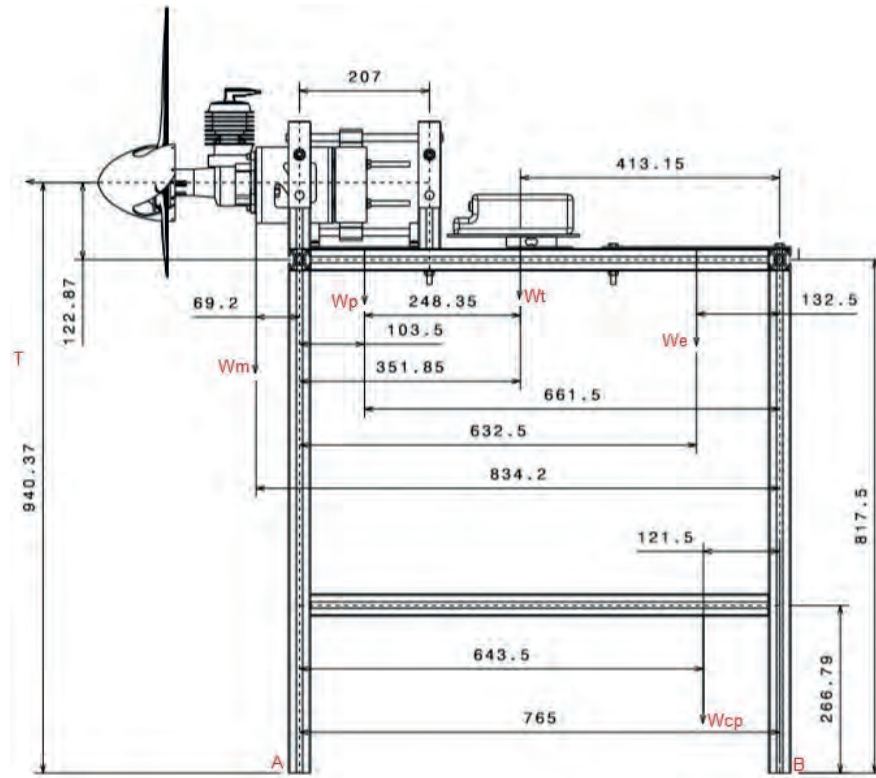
Distribución esquemática de cargas aplicadas al banco.
